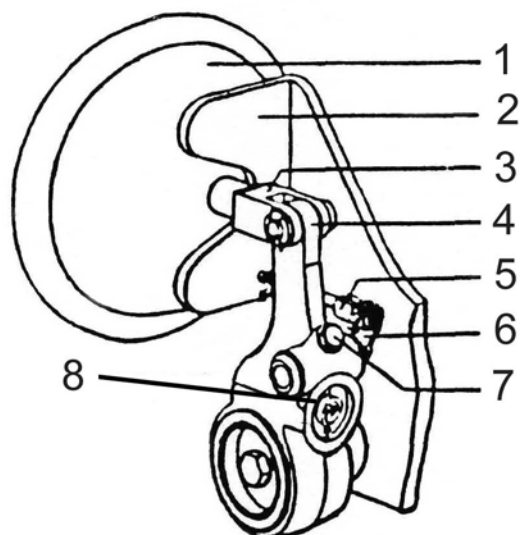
Рычаг автоматического регулирования зазора в тормозных механизмах: 1-тормозная камера; 2-кронштейн; 3-вилка штока тормозной камеры; 4-рычаг тормозной; 5-тяги; 6-регулятор тормоза с рычагом; 7-пробка; 8-фиксатор
